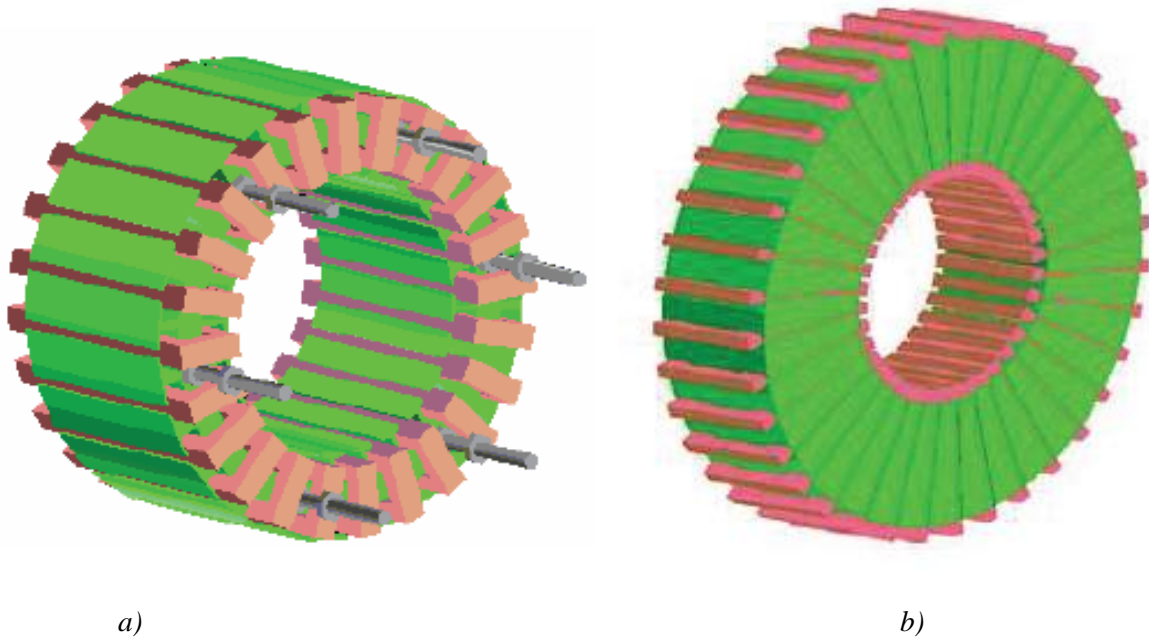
Bobinage Gramme pour machine : a) à flux radial, b) à flux axial [Bom 2009]
